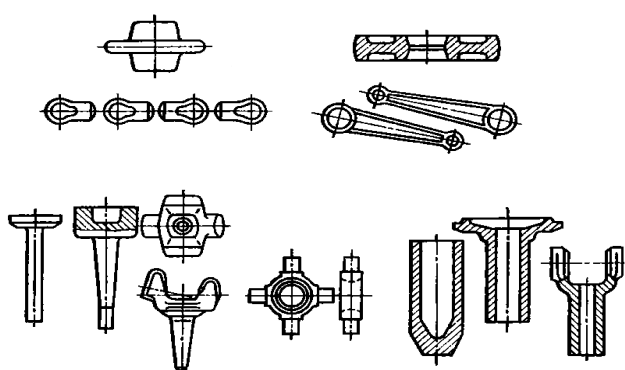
Штамповані заготовки, отримані на КГШП
